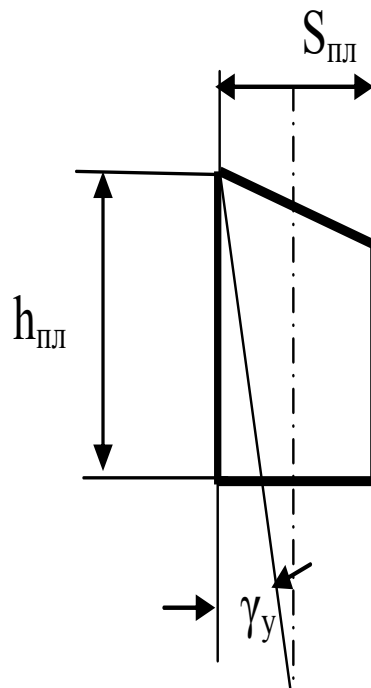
Форма поперечного сечения винтовых пластин твердого сплава по ГОСТ 25414-90:
